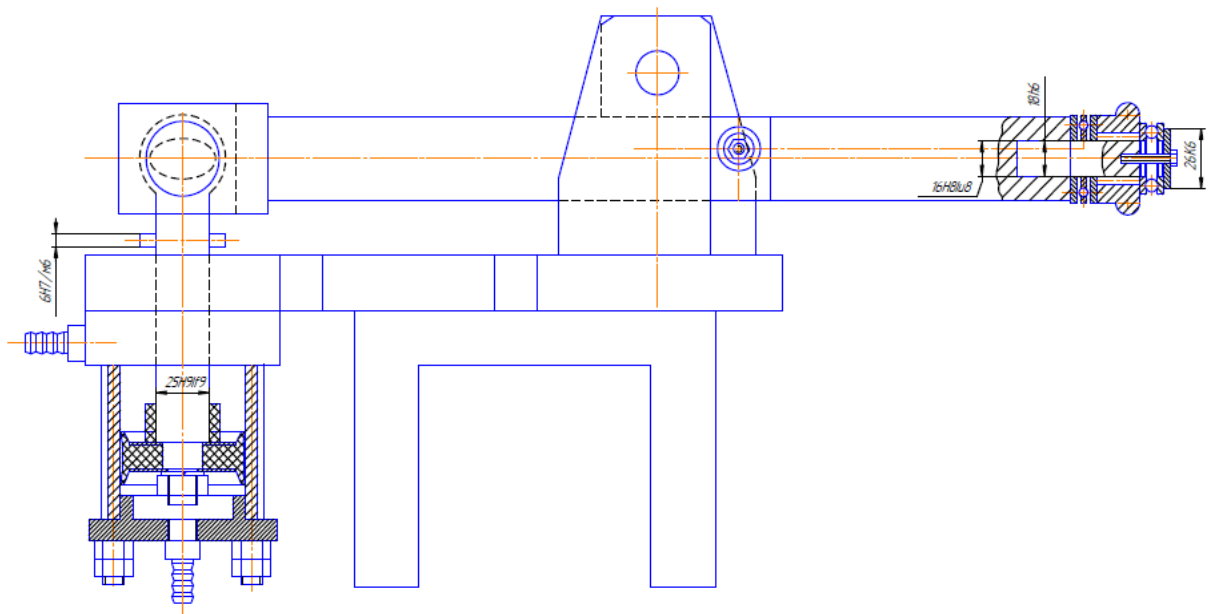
Пристосування для обкатки циліндричної деталі роликом
